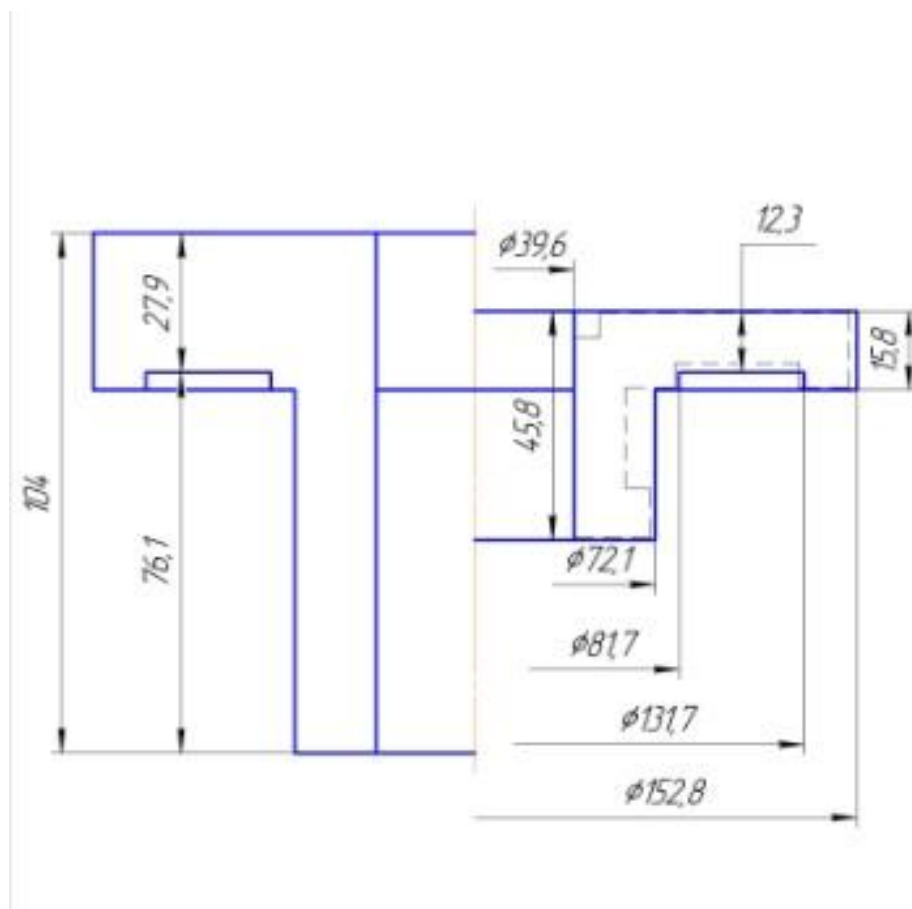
Размеры заготовки перед спеканием и размеры объема засыпки порошка в пресс-форму.
